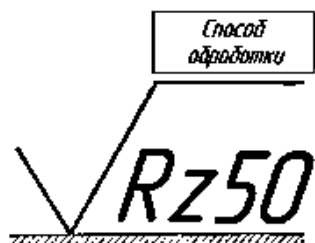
Структура обозначения шероховатости на чертеже
